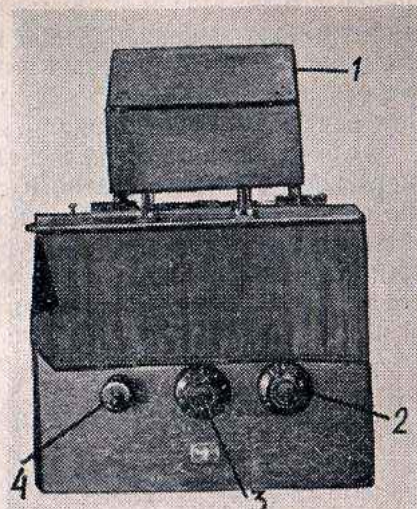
Контактный станок с понижающим трансформатором и устройством для подъема ламп: 1 — крышка; 2 — выключатель; 3 — рукоятка механизма подъема лампы; 4 — рукоятка трансформатора.
